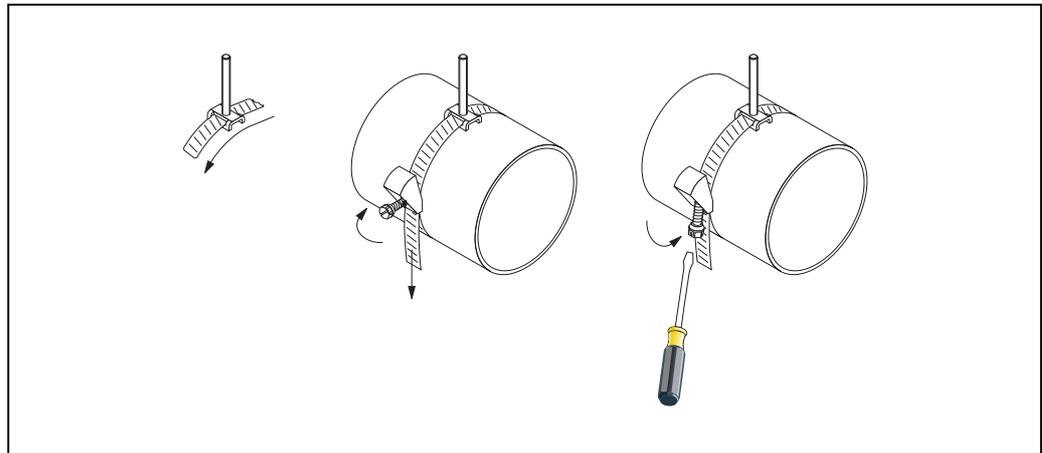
Instalação da faixa de tensionamento para DN 50...200
